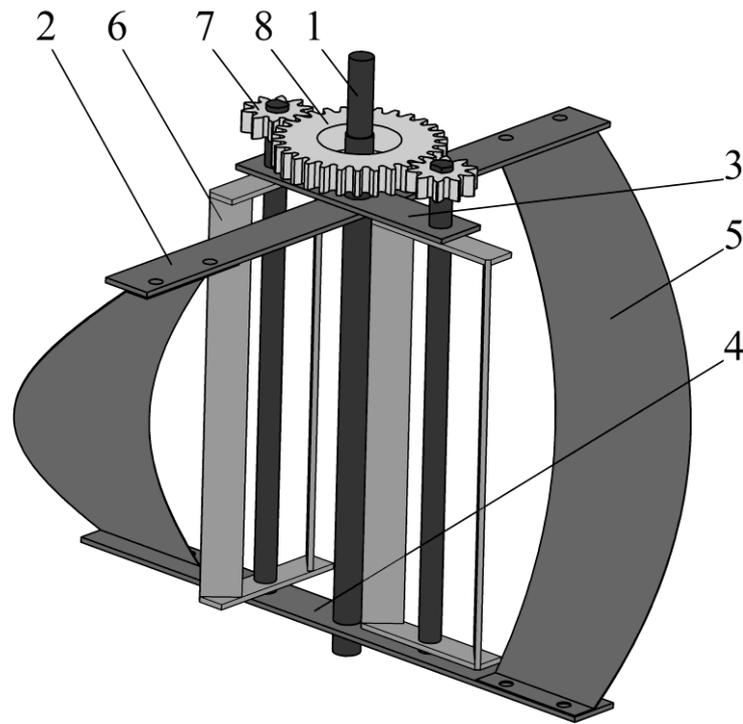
Конструкція розчинозмішувача з вертикальним шнеком та планетарними лопатями
